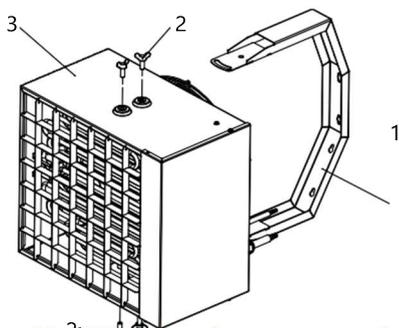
2 Installation du support mural pour le BHP- MW-15
